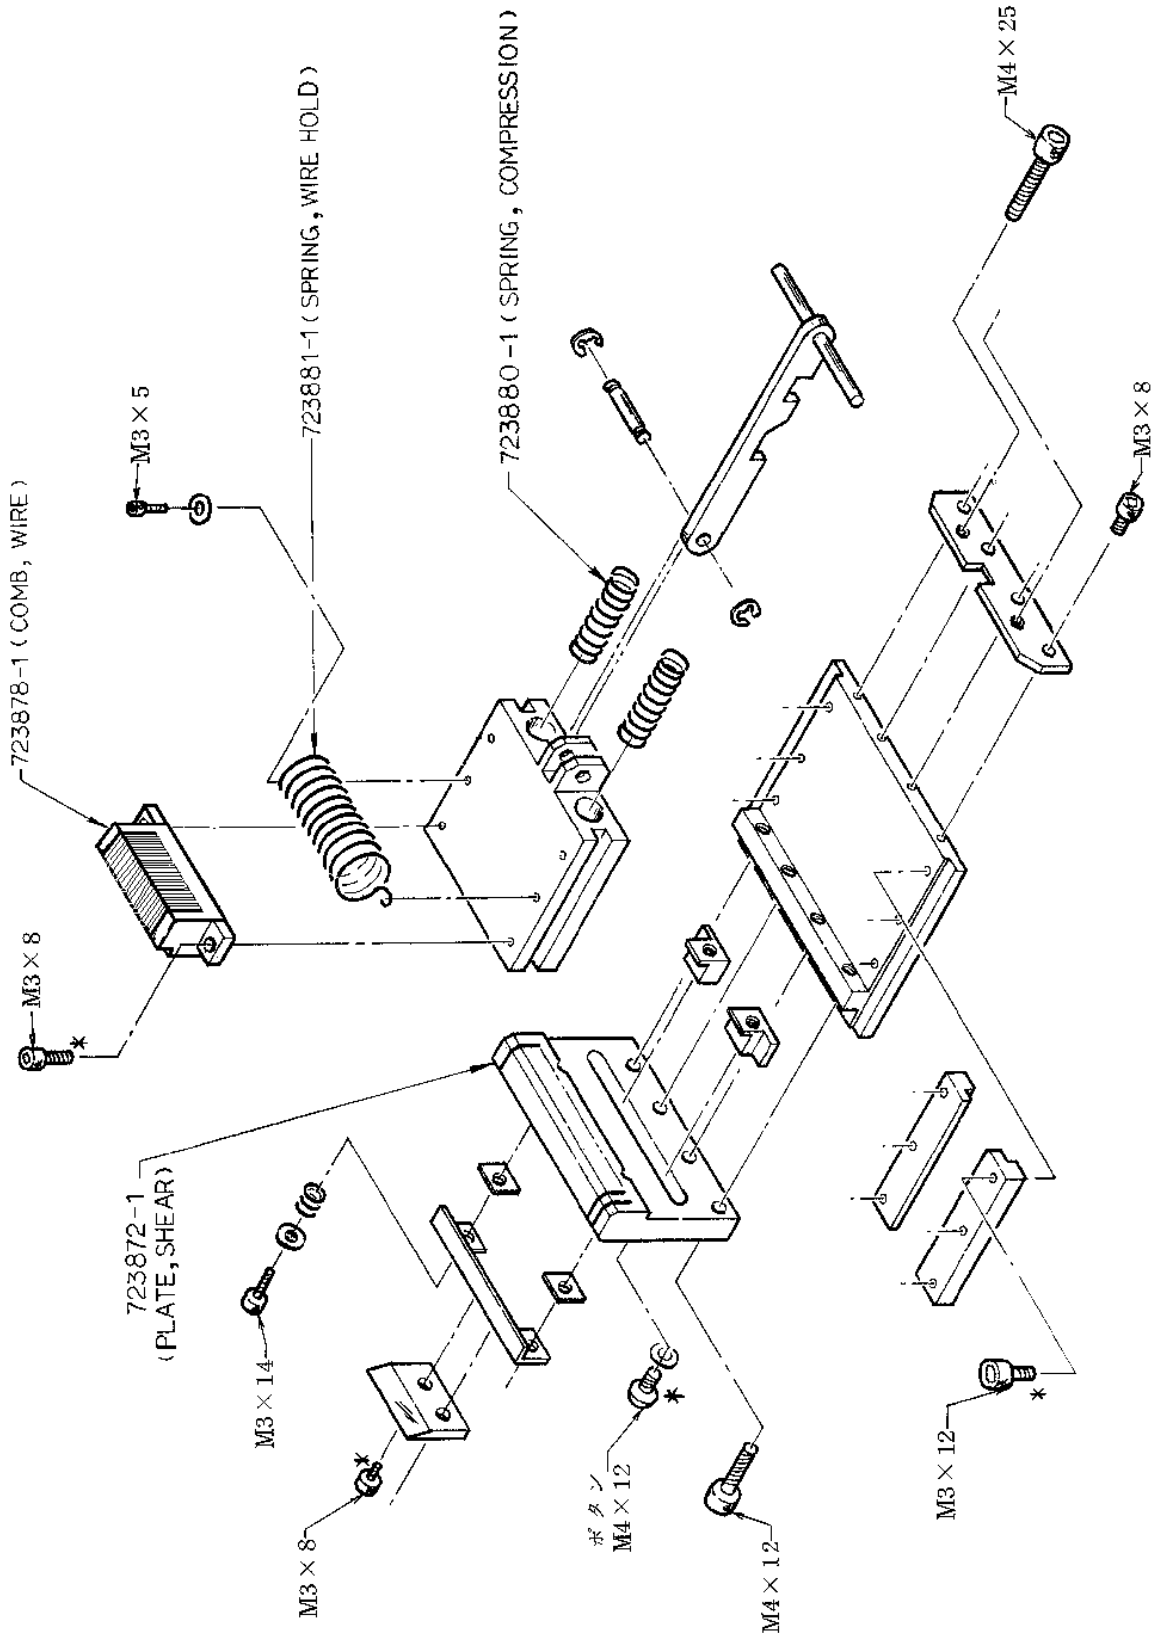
Tool Assembly for Discrete Wire Application (723860-3)
